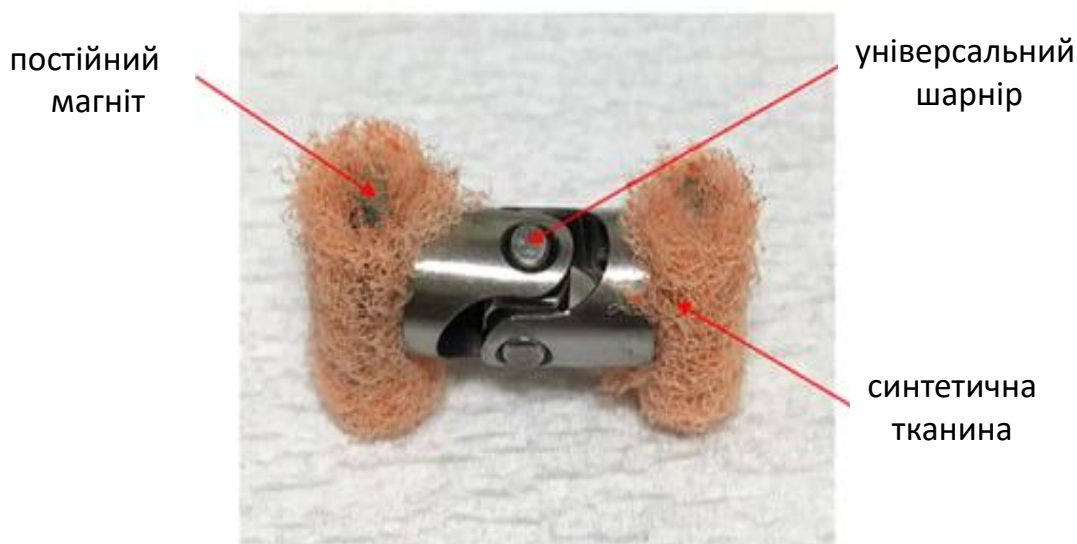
Спеціальна головка для MAO внутрішніх поверхонь вигнутих труб [33].
